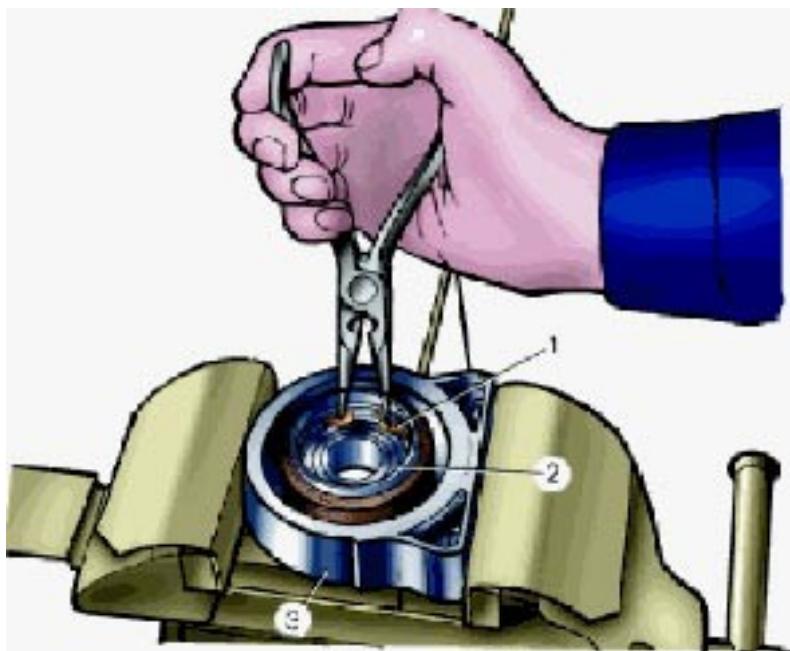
Демонтаж стопорного кільця підшипника проміжної опори:
